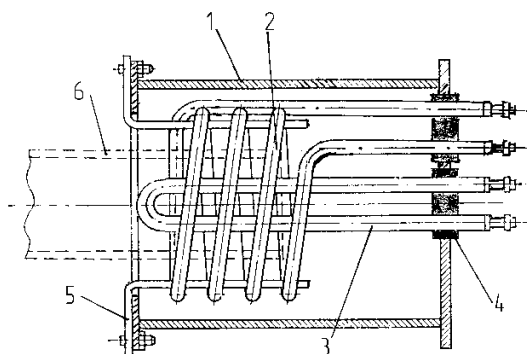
Схема нагревателя концов труб: 1 - корпус нагревателя; 2 - спиральный электронагреватель; 3 - U-образный электронагреватель; 4 - изолирующие втулки; 5 - планки крепления электронагревателей; 6 - нагреваемая труба
